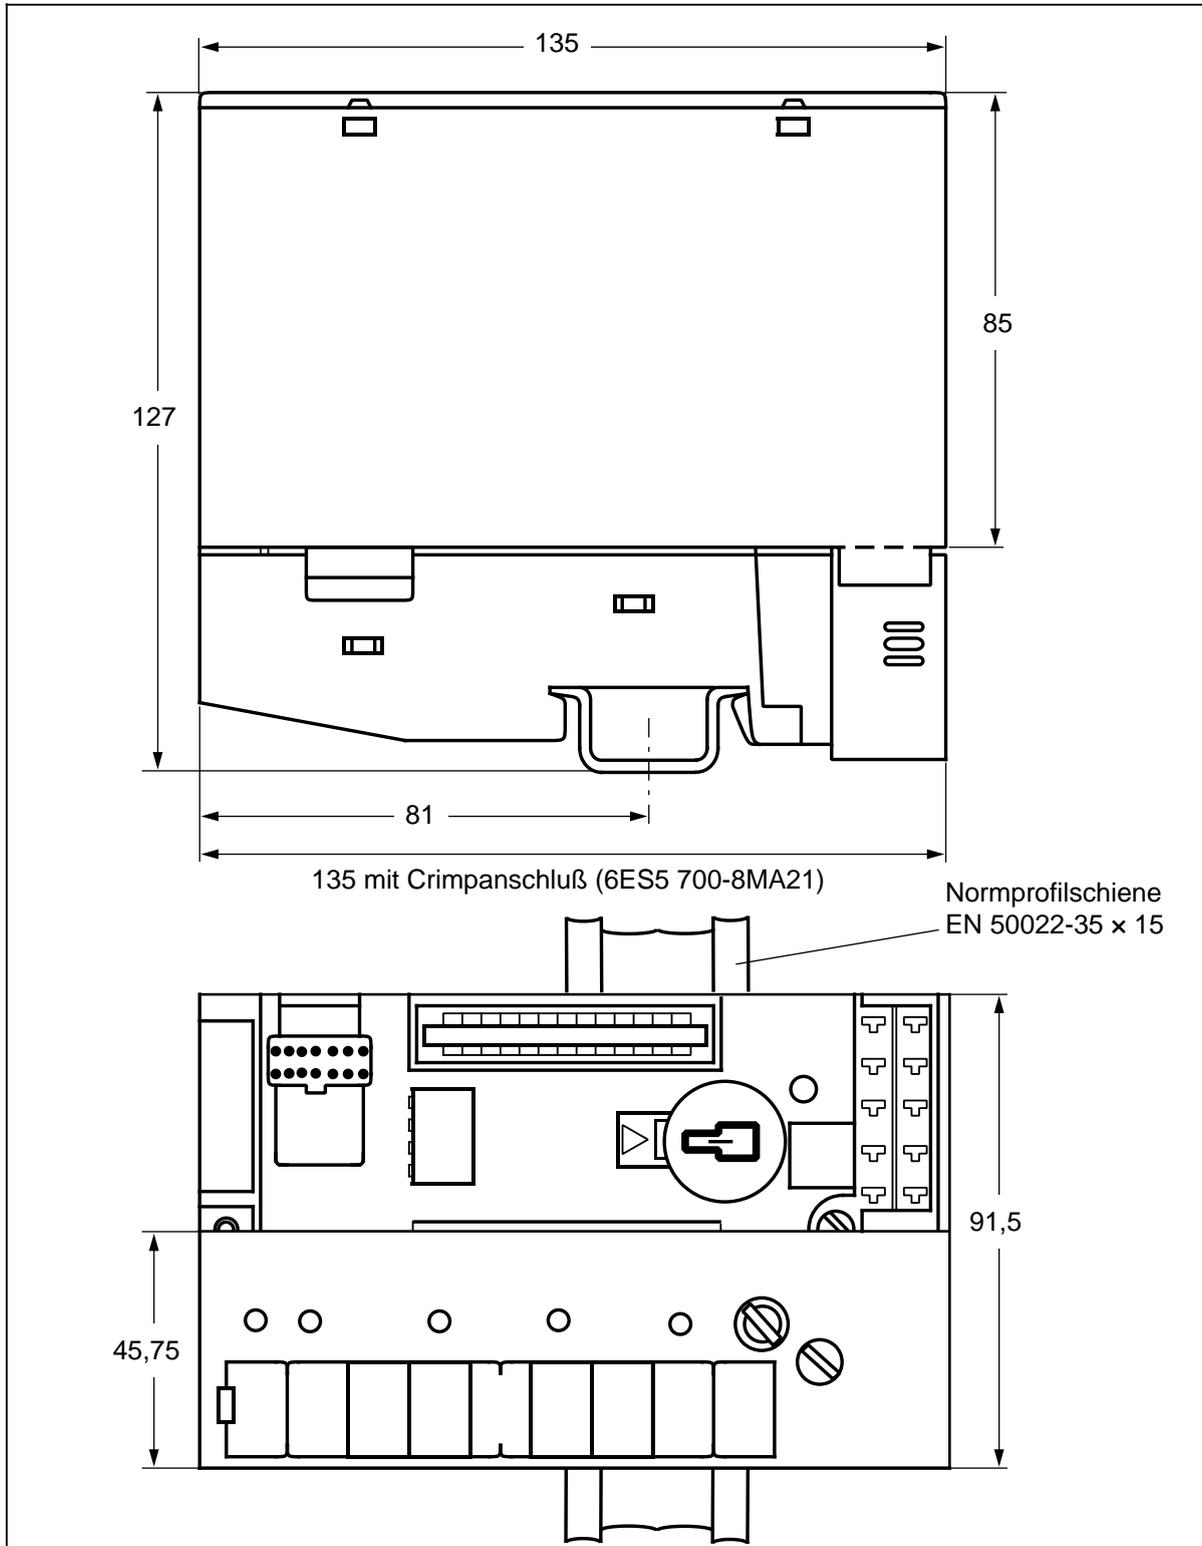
Maßbild des Busmoduls (Crimp-snap-in) mit Peripheriebaugruppe
